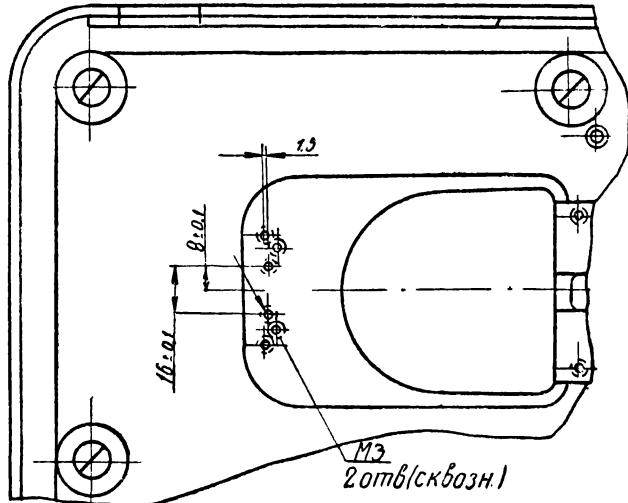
Схема дополнительной обработки корпуса — большое плато
